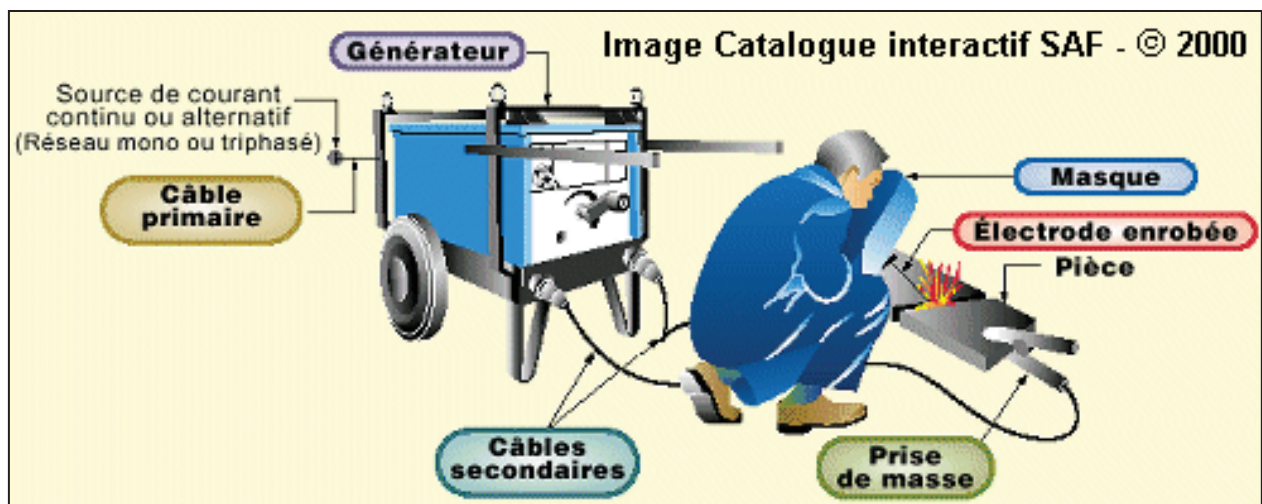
Installation pour soudage à l'électrode enrobé [9]
